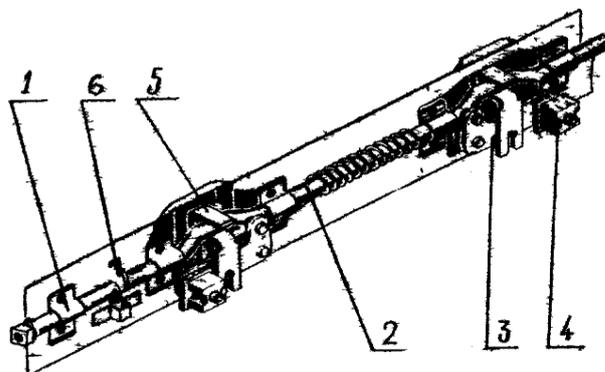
Механизм зажима решет: 1 - опора; 2 - вал коленчатый; 3 - рычаг; 4 - ползун; 5 - кронштейн; 6 - кулачок - фиксатор
